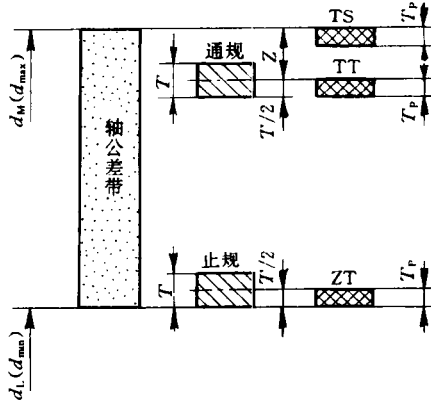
轴用工作量规及其校对量规定形尺寸公差带示意图
